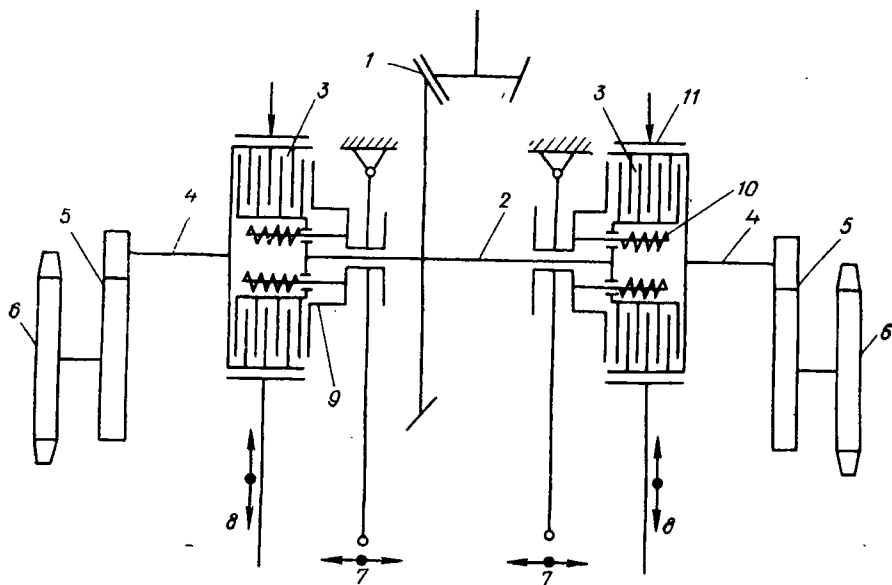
4. Схема управления поворотом трактора с помощью бортовых фрикционов: 1 — главная передача; 2 — вал бортовых фрикционов; 3 — фрикционные муфты управления; 4 — валы ведущих шестерен; 5 — концевая (бортовая) передача; 6 — ведущая звездочка; 7 — приводы выключения фрикционных муфт; 8 — приводы тормозов; 9 — нажимная тарелка; 10 — нажимные пружины; 11 — ленточный тормоз.
